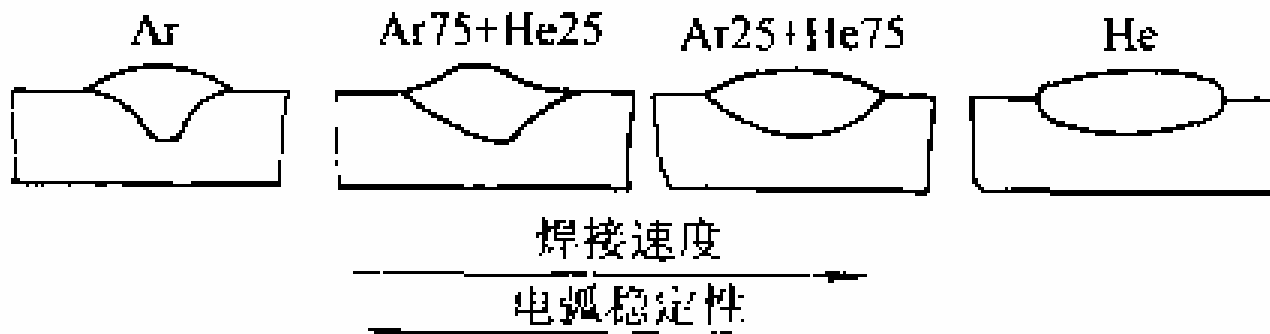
MIG 焊（长弧）焊接铝合金，
